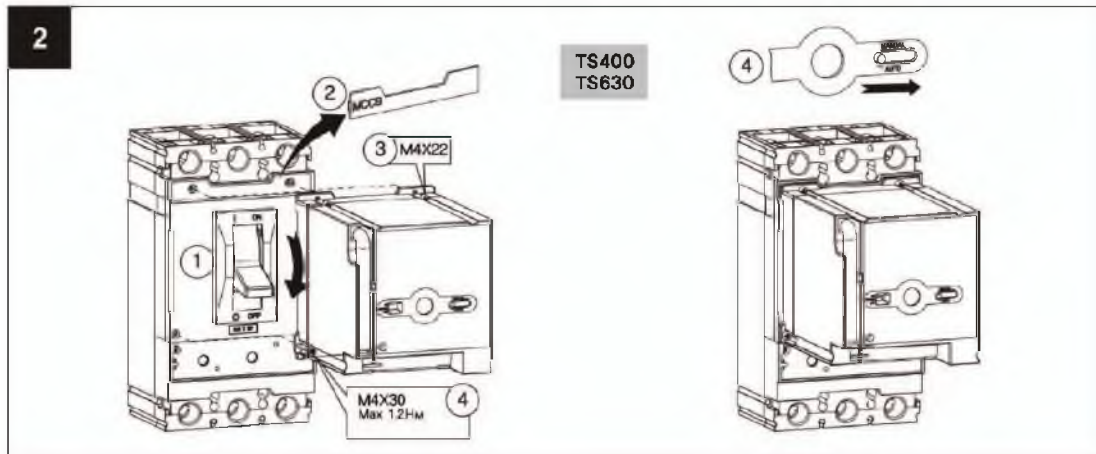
Установка моторного привода на выключатели TS400 и TS630
